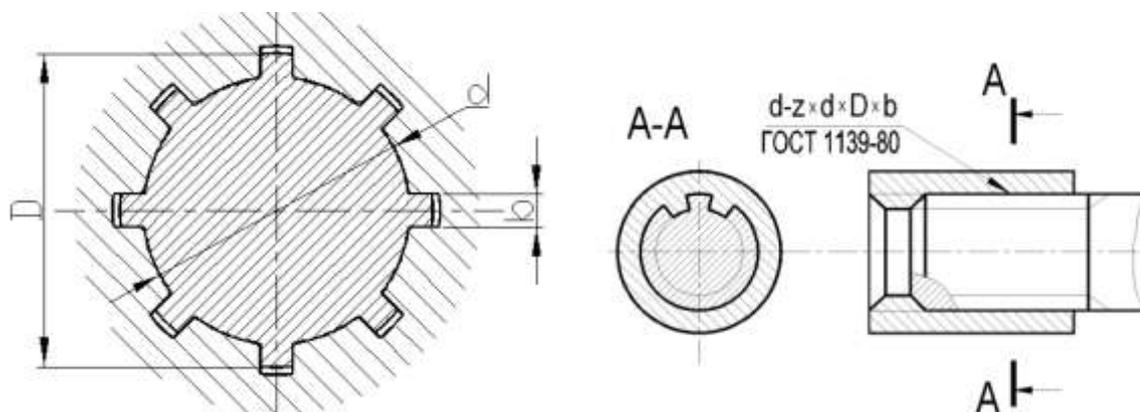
Шлицевое соединение: а) прямобоочный профиль шлица; б) изображение и обозначение прямобоочного зубчатого соединения
